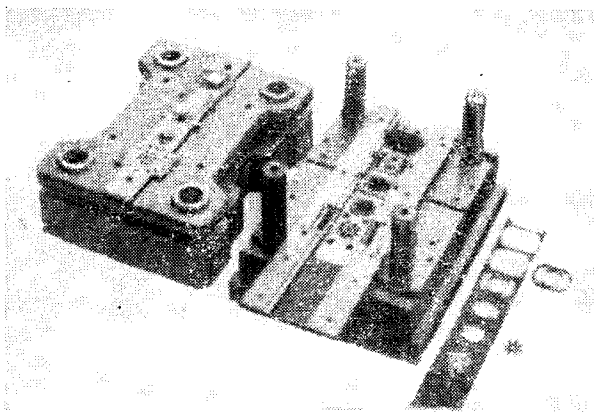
Армированный твердым сплавом штамп для вырубки деталей из листовой стали для статоров и роторов электродвигателей
